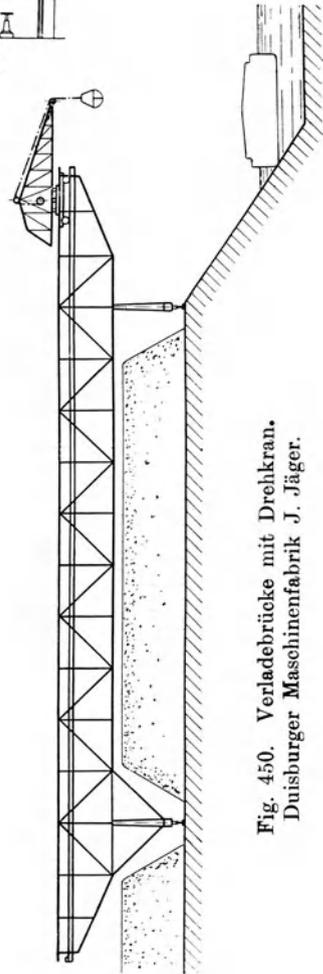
Verladebrücke mit Drehkran. Duisburger Maschinenfabrik J. Jäger.
